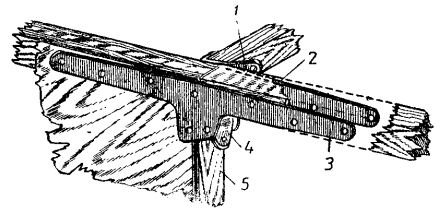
Верхний узел разъема фюзеляжа. 1—ушко для крепления верхней расчалки; 2—верхний лонжерон задней части фюзеляжа; 3—щека узла; 4—ушко для крепления вертикальной расчалки; 5—стойка.
